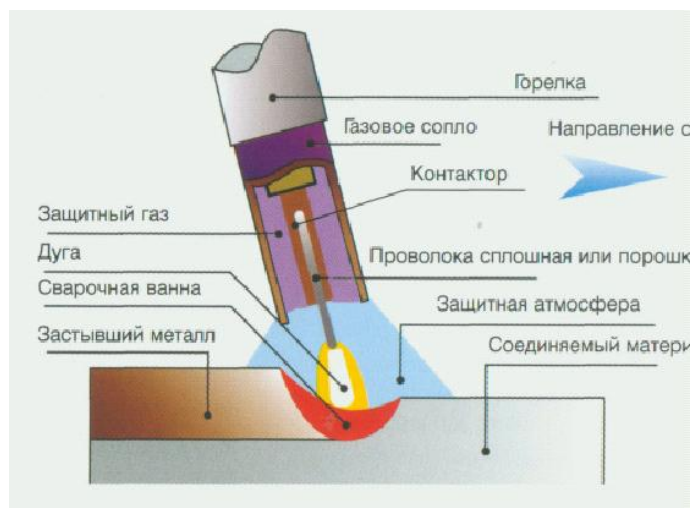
Полуавтоматическая сварка в среде защитного газа
